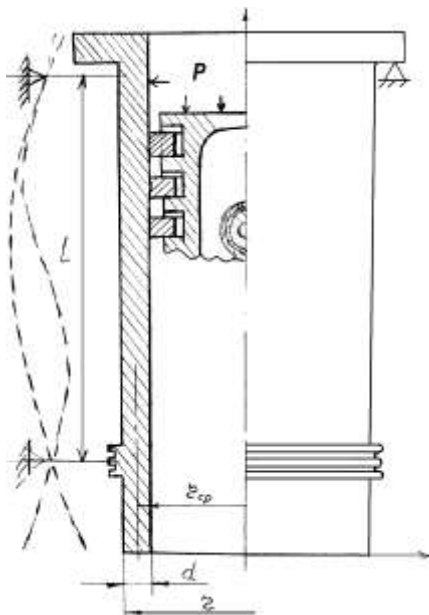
Типовая схема цилиндровой втулки тронкового двигателя
